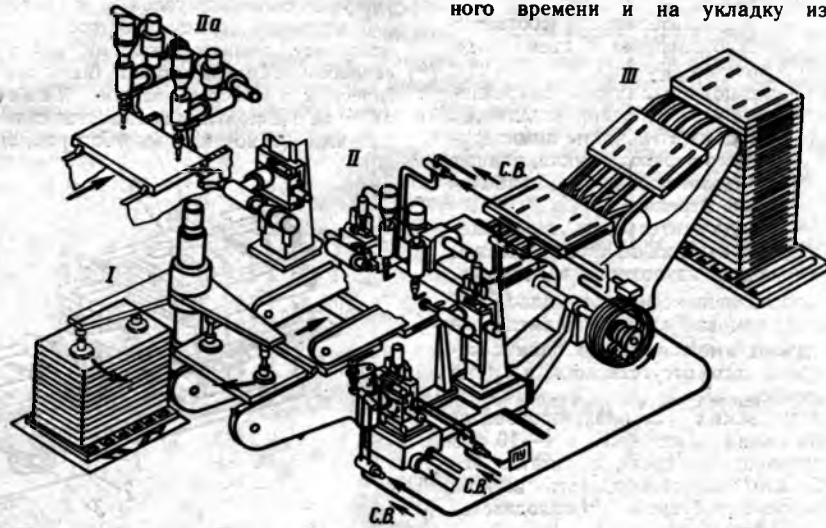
Модуль сверлильно-фрезерного автомата для обработки щитов
